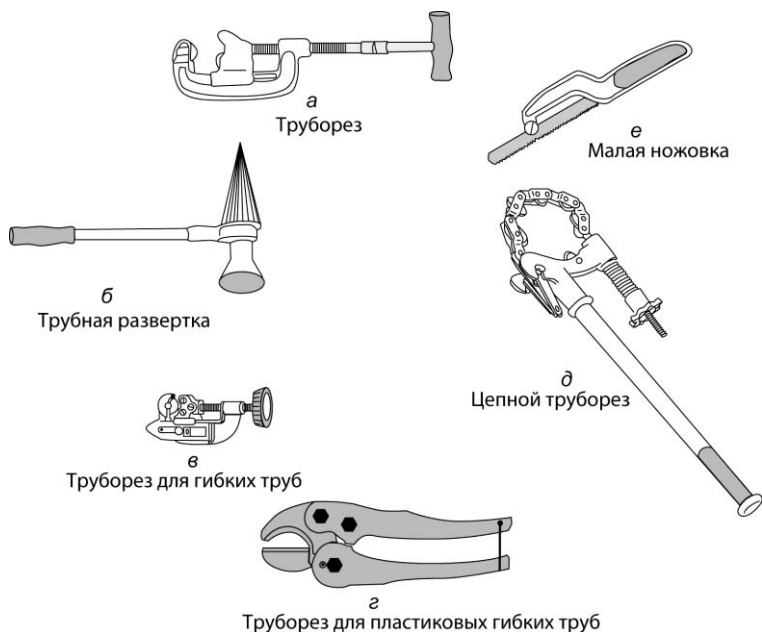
Специальные инструменты для резки труб: труборез (а); трубная развертка (б); труборез для гибких труб (в); труборез для пластиковых гибких труб (е); цепной труборез (д); малая ножовка (е)
